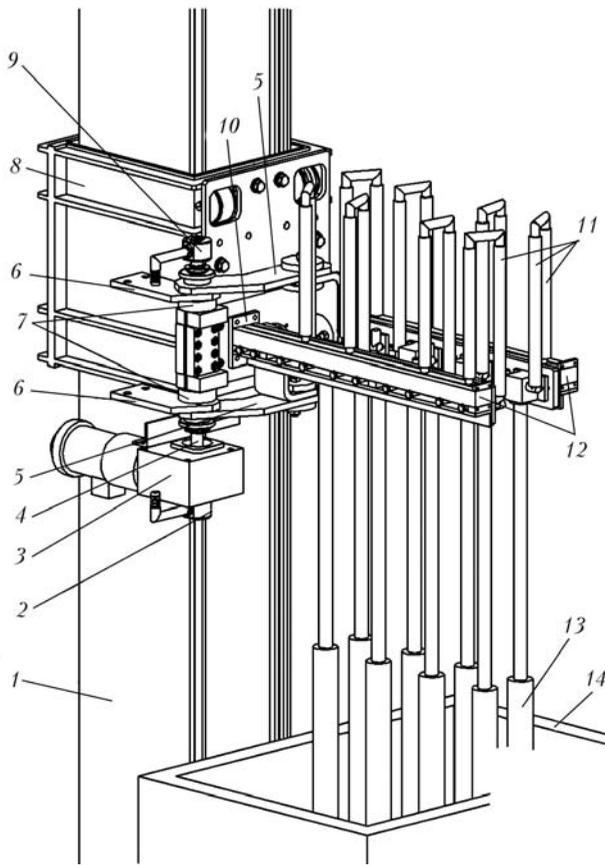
Конструкция поворотного механизма: 1 – колонна; 2 – муфта; 3 – электромеханический привод; 4 – вал механизма поворота; 5 – шины токоподводящие; 6 – соединители; 7 – шарниры шин; 8 – каретка нижняя; 9 – муфты; 10 – фланцы подвода воды; 11 – элементы системы охлаждения; 12 – кронштейны передвижные; 13 – нерасходуемые электроды; 14 – тигель
